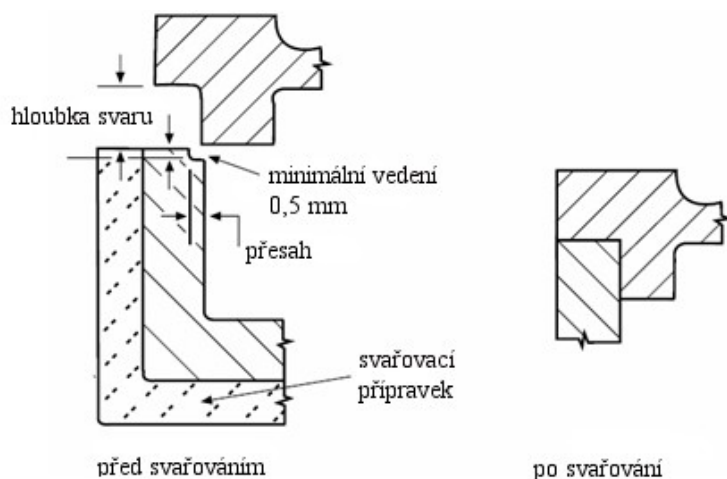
Spoj pero - drážka [10, s. 22]
